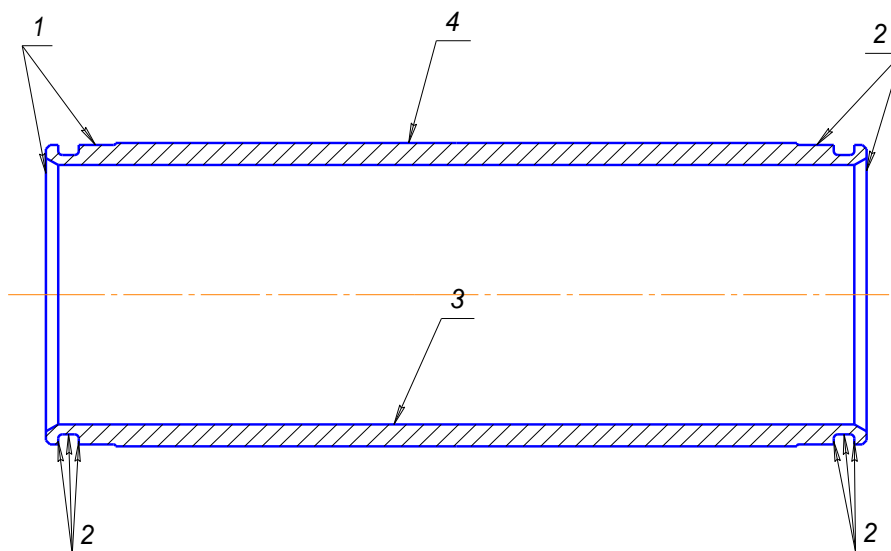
Классификация поверхностей детали – цилиндр гидроамортизатора
